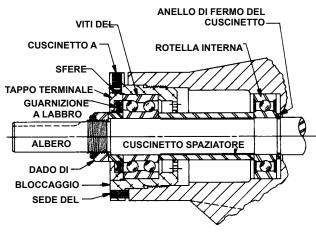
ASSEMBLAGGIO SEDE DEL REGGISPINTA AS, AK E AL
